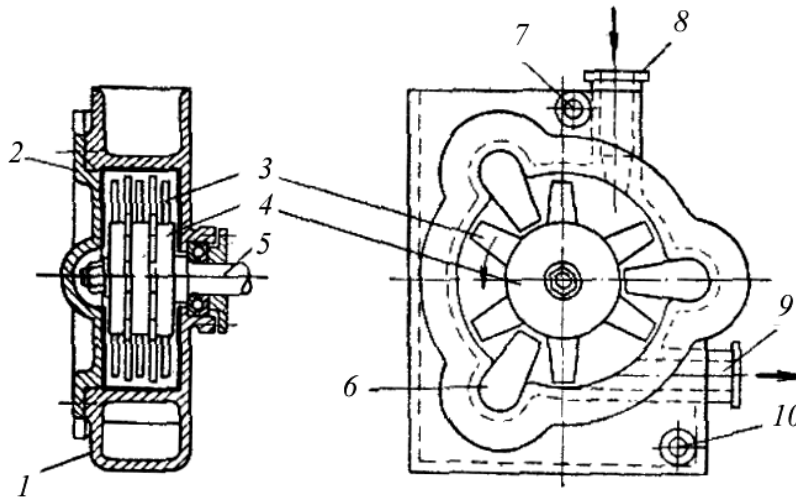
Роторно-бильний колоїдний млин:
